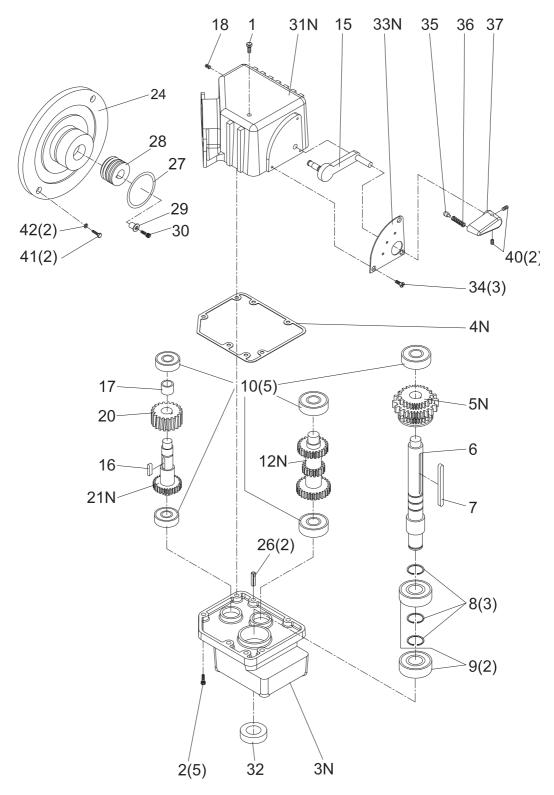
Explosionszeichnung Getriebe - Explosion drawing gear: 712 fifth generation
